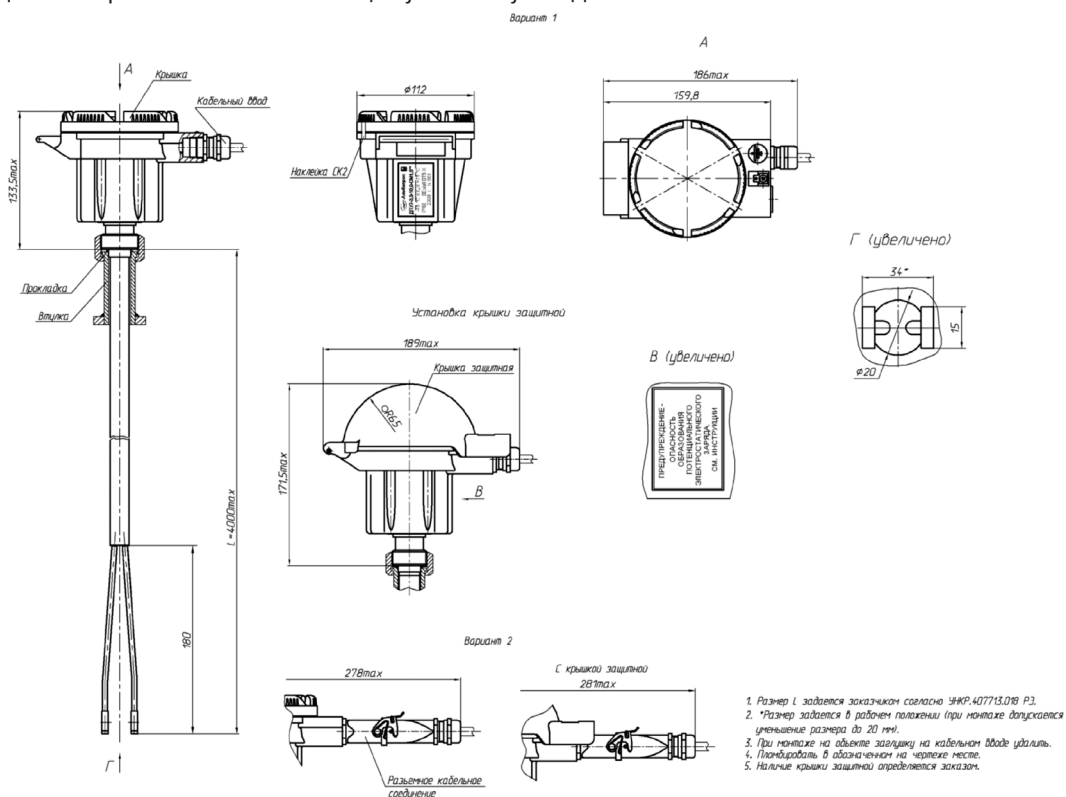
Габаритные размеры датчика ДПУ7
